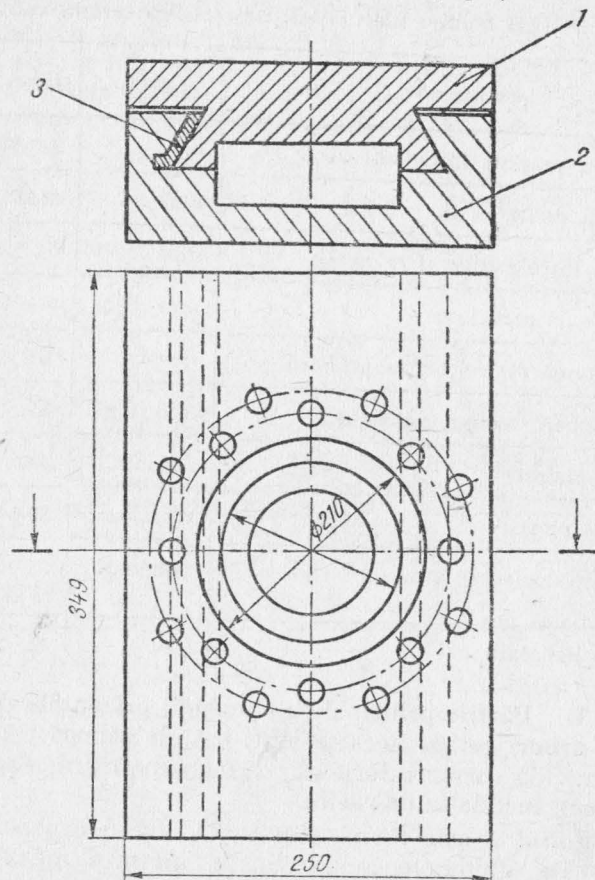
Dispozitivul de prindere a piesei la mașina de rectificat arbori cotați.
